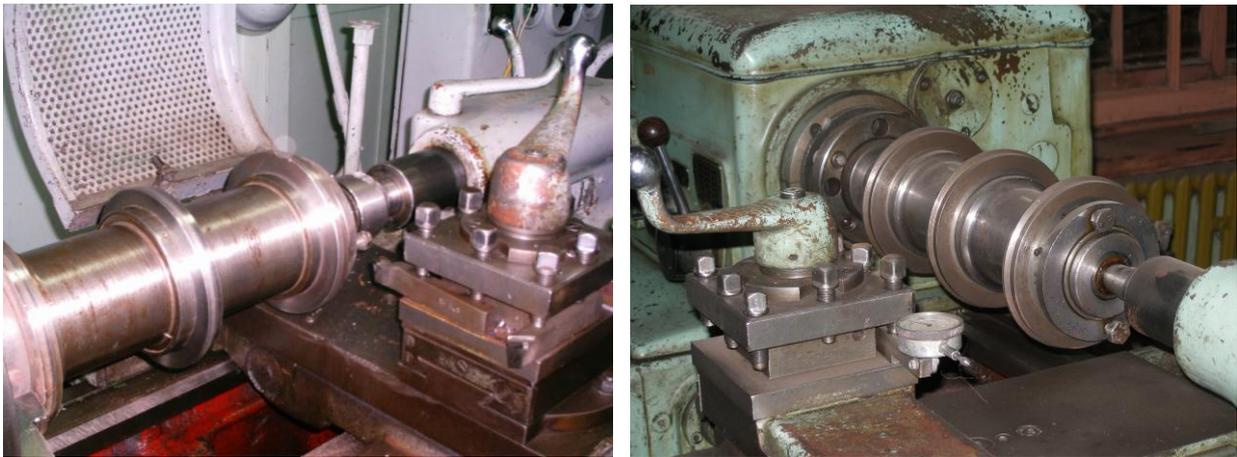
Оправка с тремя кольцами в центрах токарного станка
